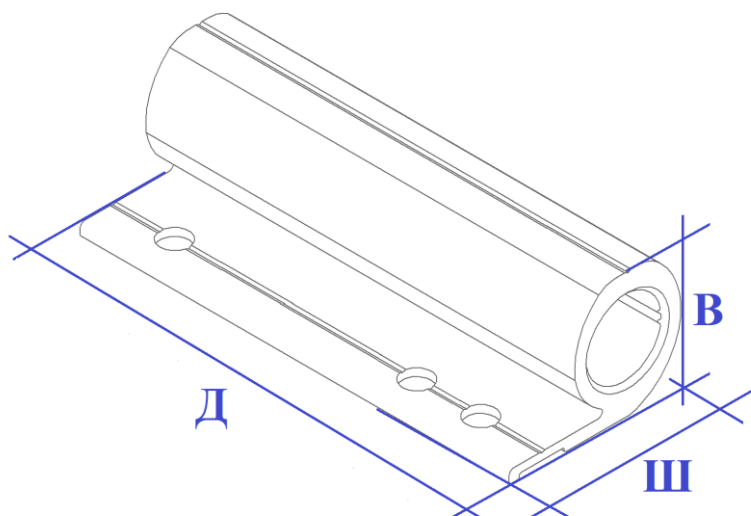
Габаритные размеры корпуса сигнализатора
